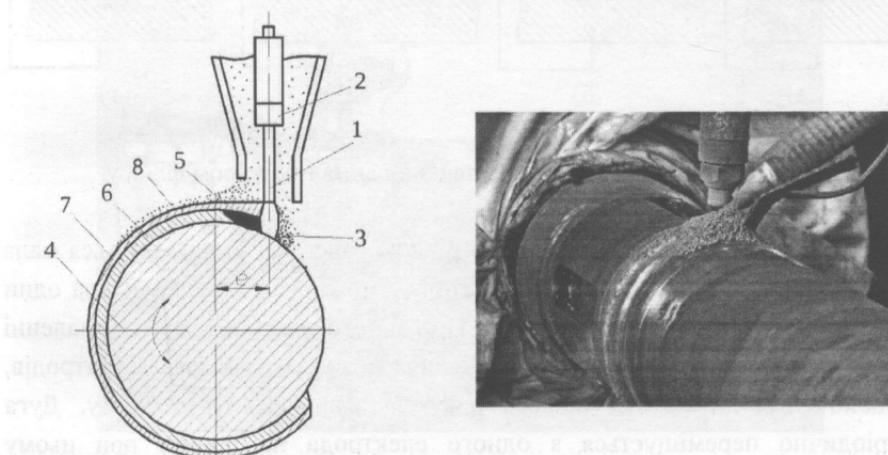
Схема та загальний вигляд наплавлювання під шаром флюсу
